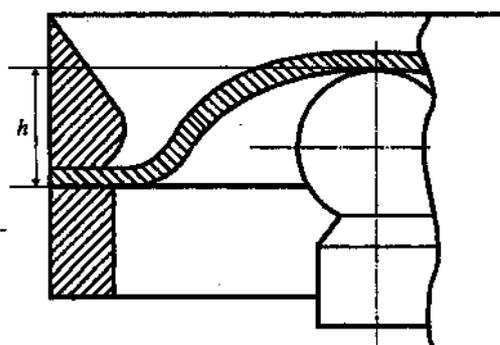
Схема испытаний на вытяжку сферической лунки
